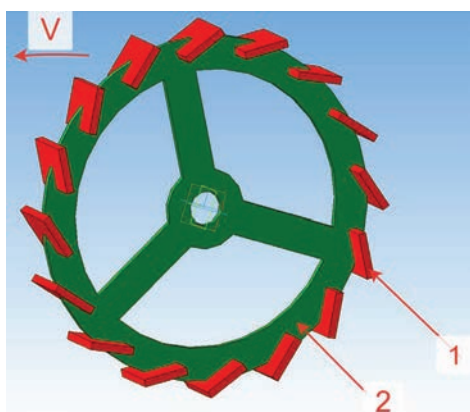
Конструкция кольчато-шпорового почвообрабатывающего рабочего органа:
